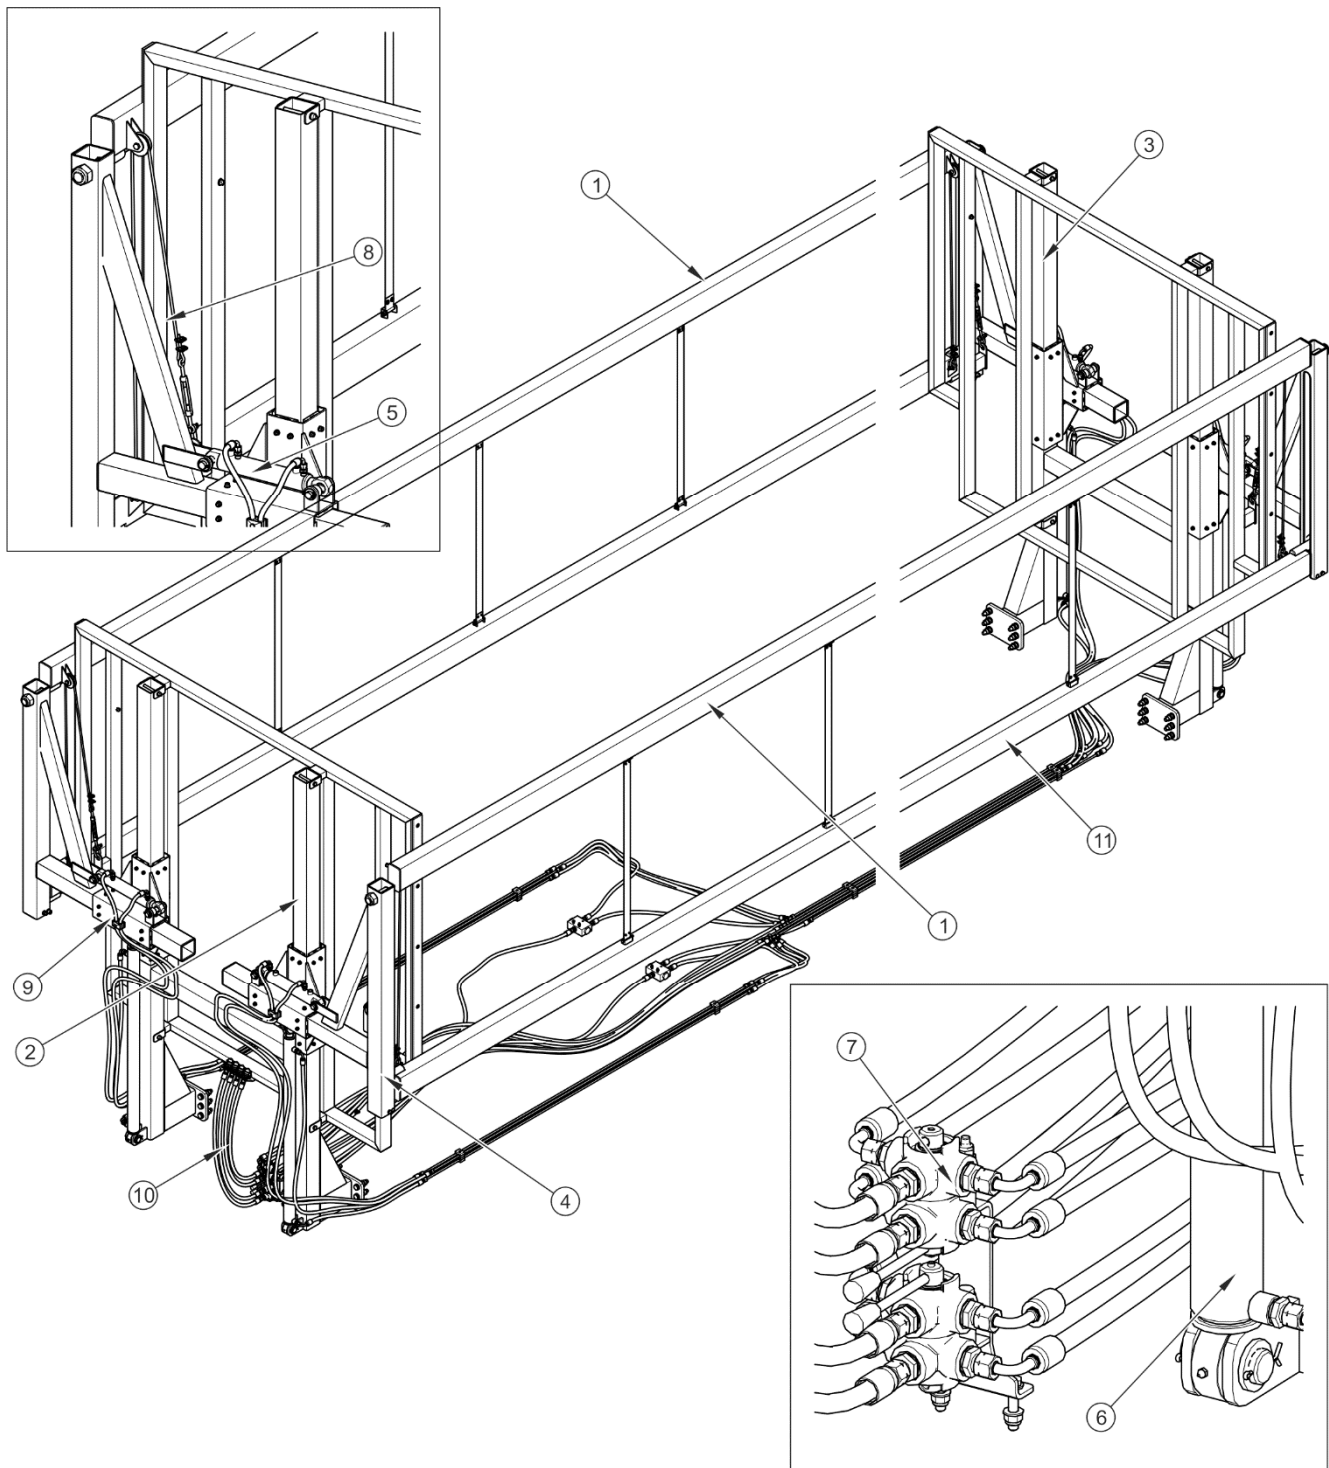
Construction du système hydraulique de relevage des parois
